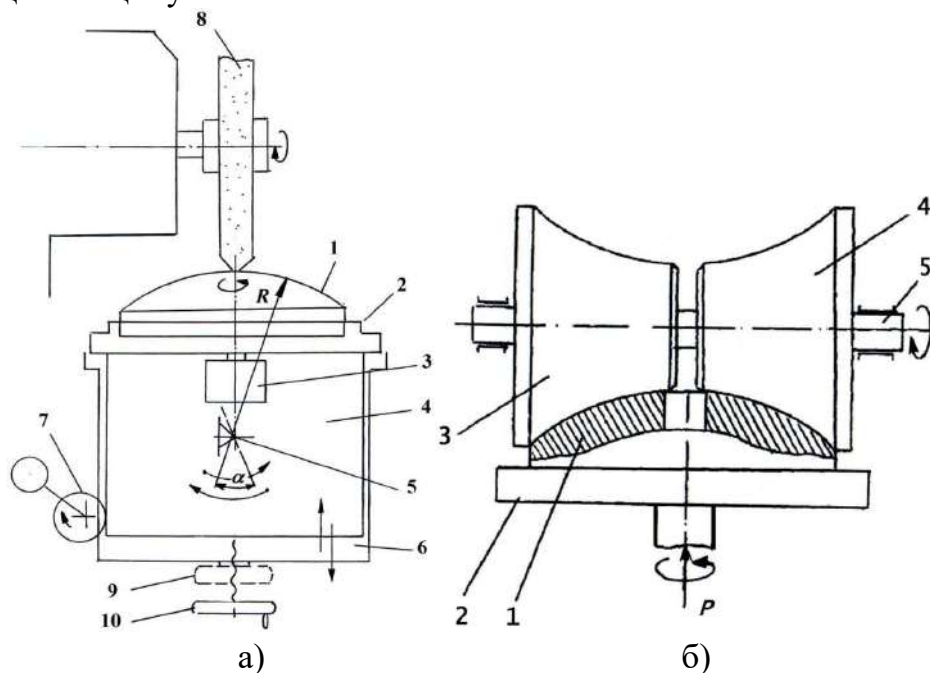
а) Схематичний пристрій зміцнювального пристосування: 1 – розподільник; 2 – патрон; 3 – мотор-редуктор для обертання патрона з розподільником; 4 – плато; 5 – вісь хитання плато; 6 – супорт; 7 – механізм хитання плато навколо осі 5; 8 – шліфувальний круг; 9 – динамометр; 10 – маховик супорта; б) Пристрій для зміцнення розподільників: 1 – розподільник; 2 – шайба верстата; 3, 4 – профільні зміцнювальні диски; 5 – вісь
